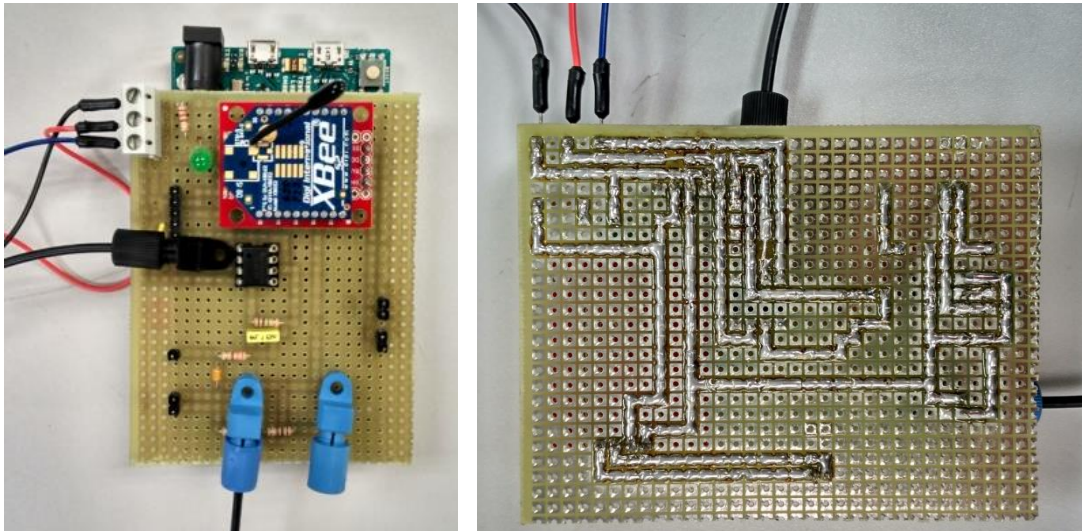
Parte delantera (Izquierda) y trasera (Derecha) del circuito soldado sobre una placa perforada
